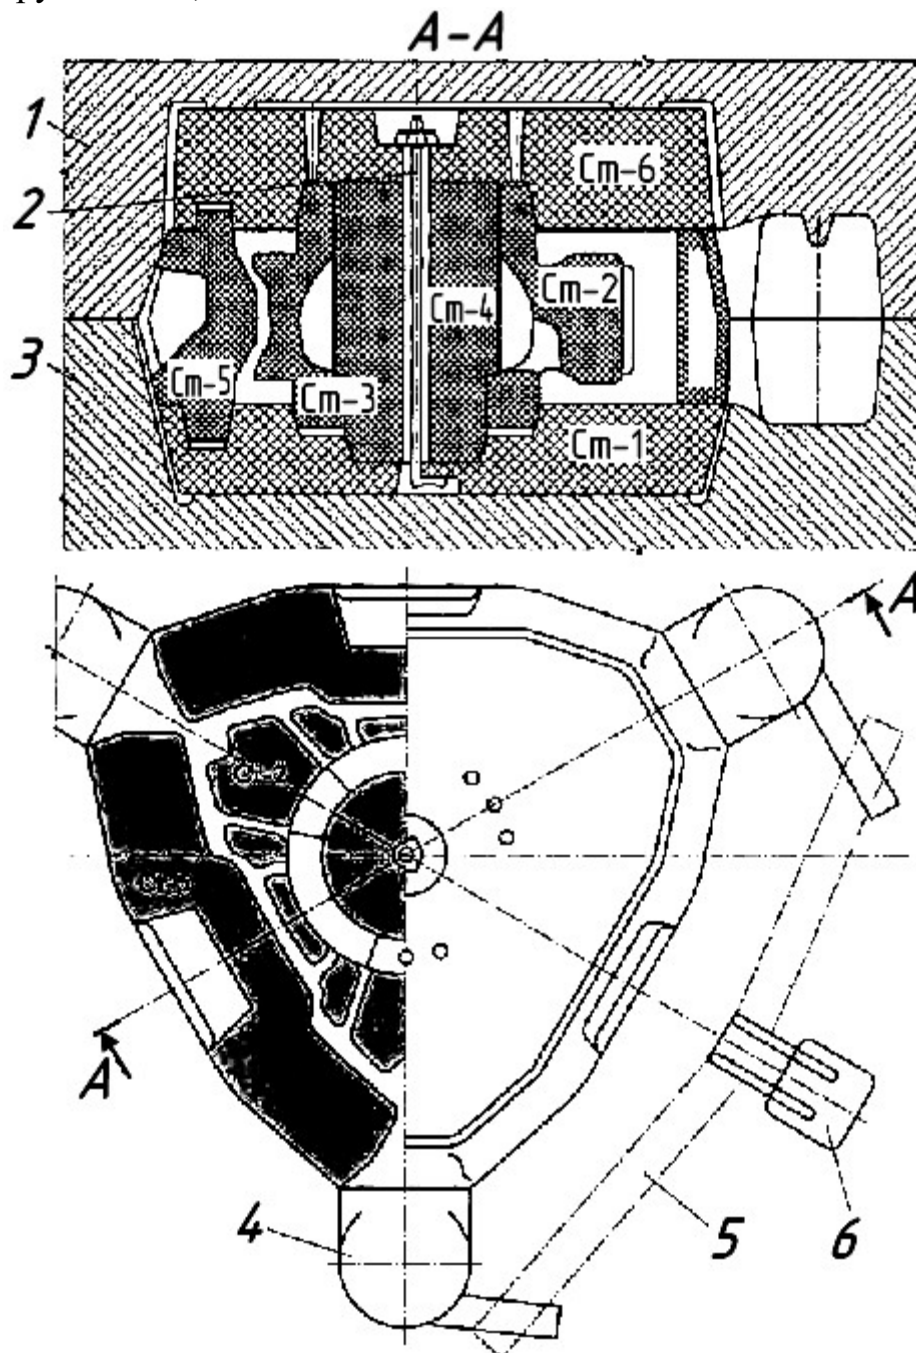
Формовка в стержнях: 1 – верхняя полуформа; 2 – шпилька; 3 – нижняя полуформа; 4 – прибыль; 5 – литниковый ход; 6 – дроссель; Ст-1 – Ст-6 – стержни
